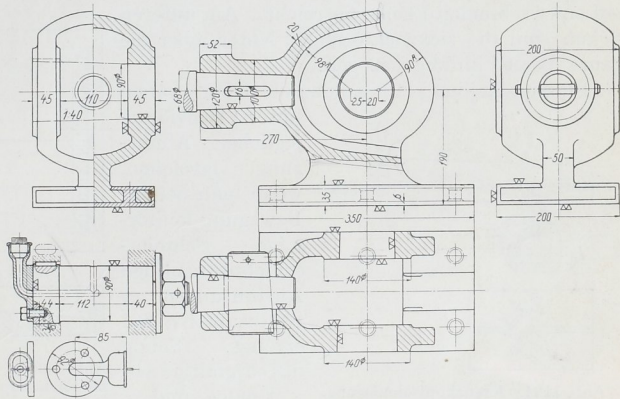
Kreuzkopf mit einseitiger Führung. M. 1 : 10.
